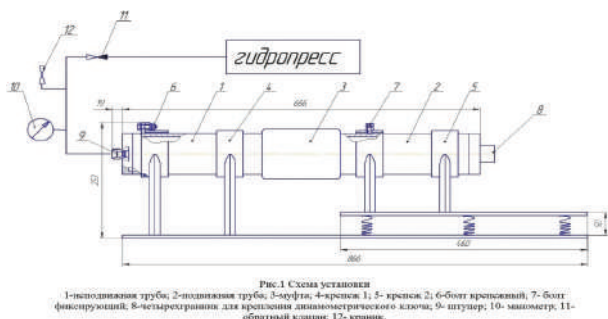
Схема установки для изучения герметизирующих свойств резьбовых смазок
